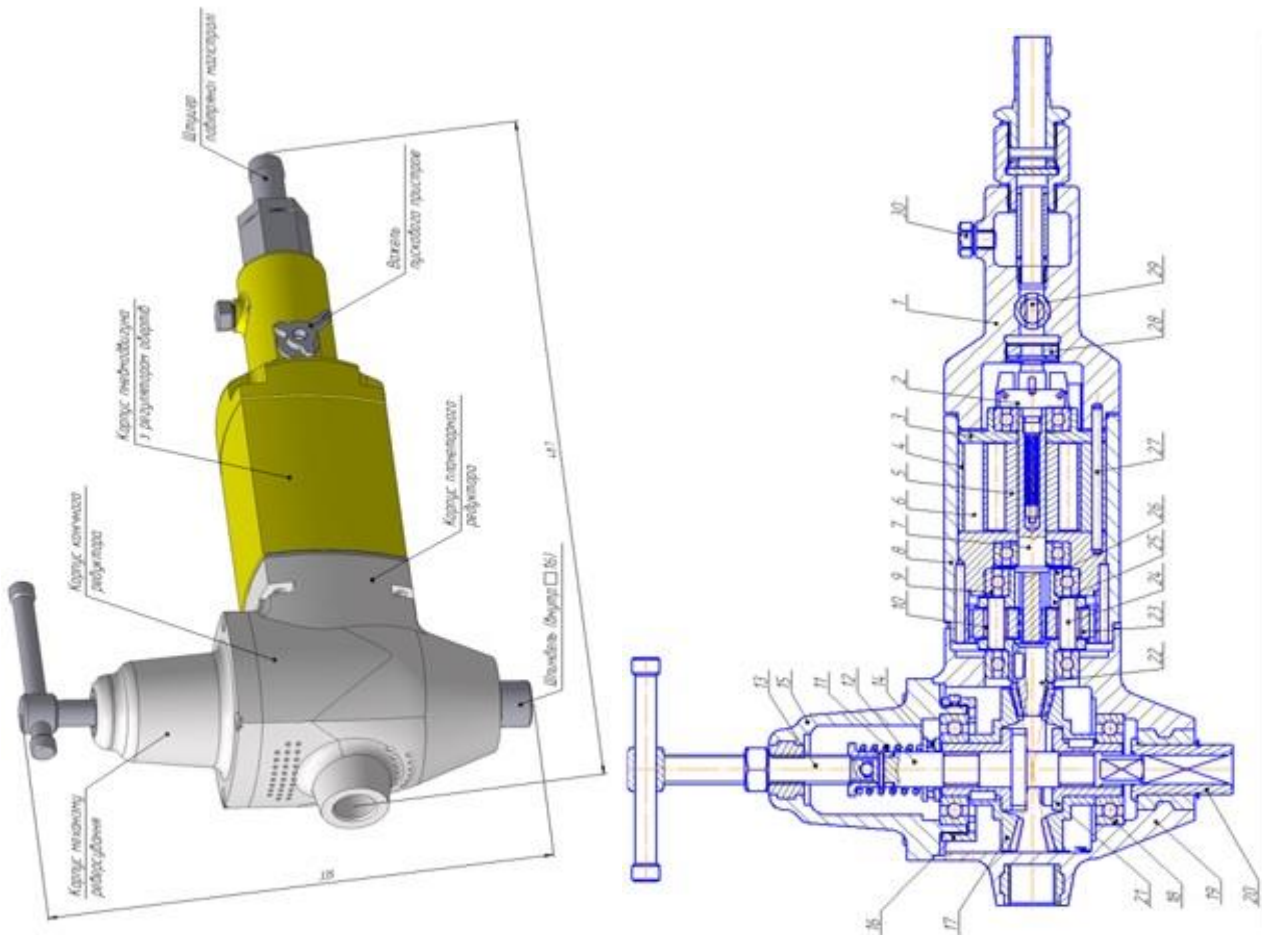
3Д зображення та поздовжній розріз приводної пневматичної реверсної машини ХТ 7809-0527
